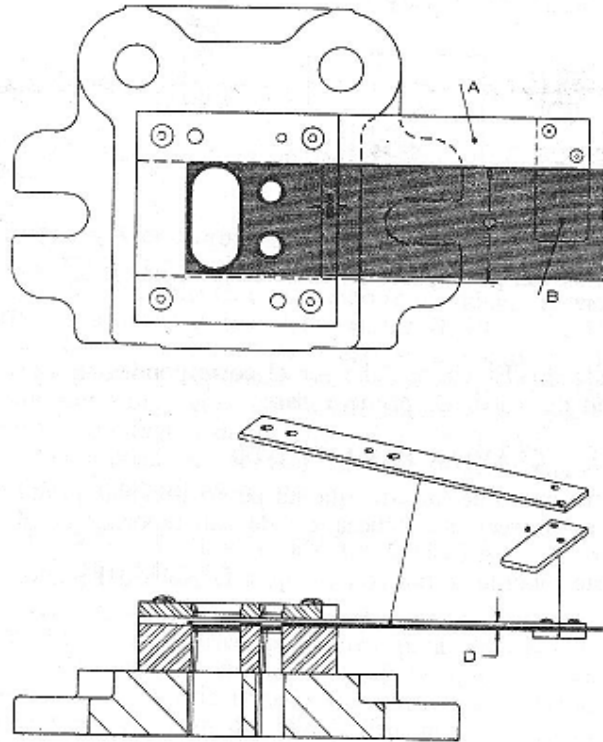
Posicionamiento de la tira de recorte mediante placa guía
